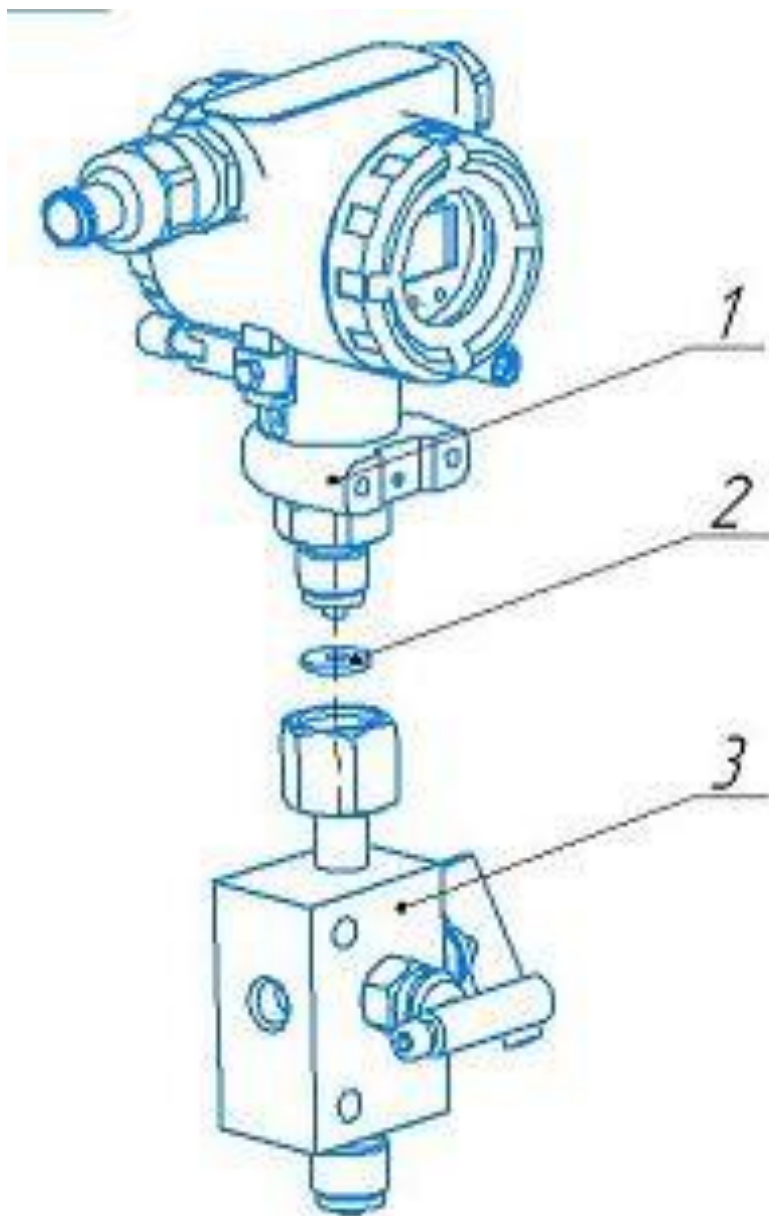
Схема сборки датчика с запорным клапаном типа КЗИК-23.02
